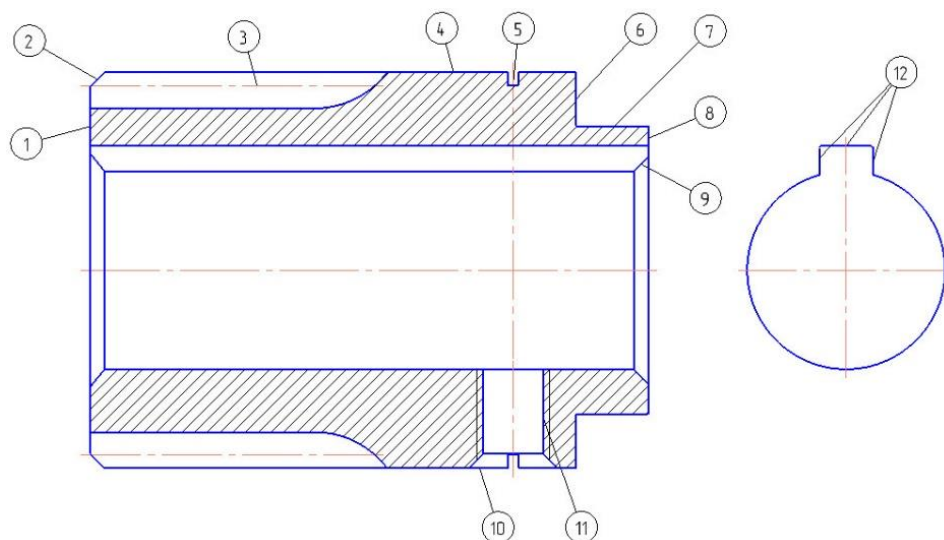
Ескіз шестерні з позначенням поверхонь.
